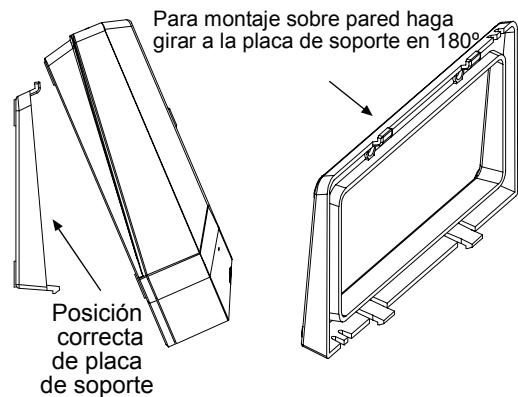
Montaje sobre Pared-Posición correcta de la Placa de Soporte
